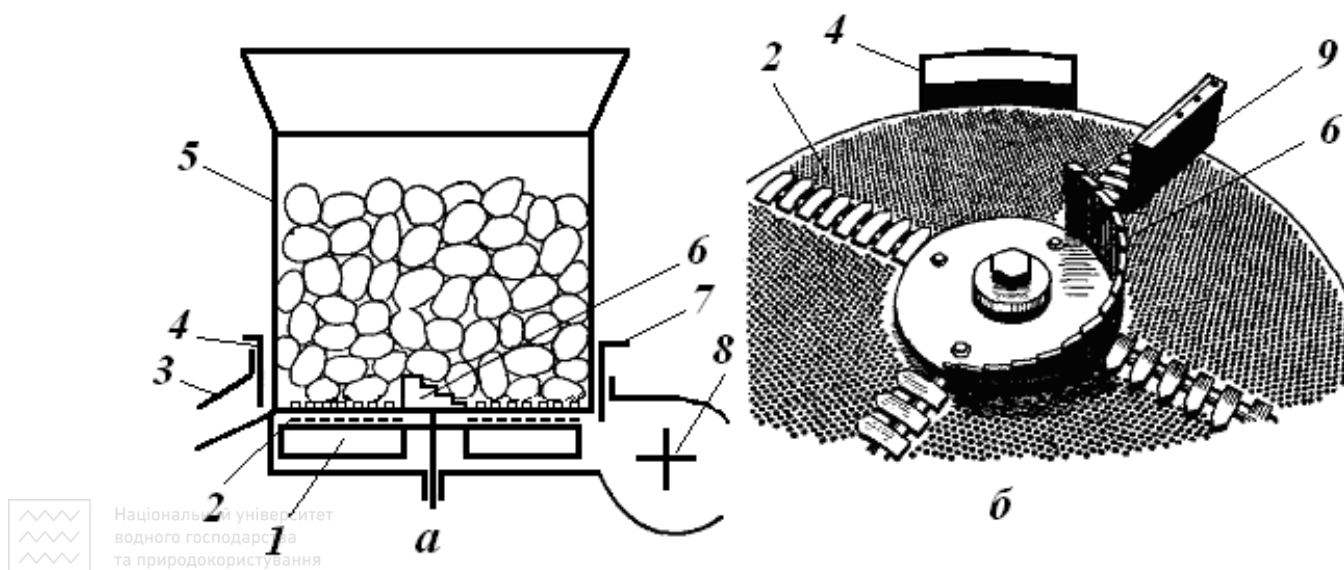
Подрібнювач-змішувач добрив ИСУ-4: а - функціональна схема; б - робочий орган; 1 - вивантажувальні лопаті; 2 - решето; 3 - потік; 4 - заслінка для вивантажування домішок; 5 - бункер; 6 - подрібнювач; 7 - заслінка для вивантажування добрив; 8 - ротор; 9 - шибер
